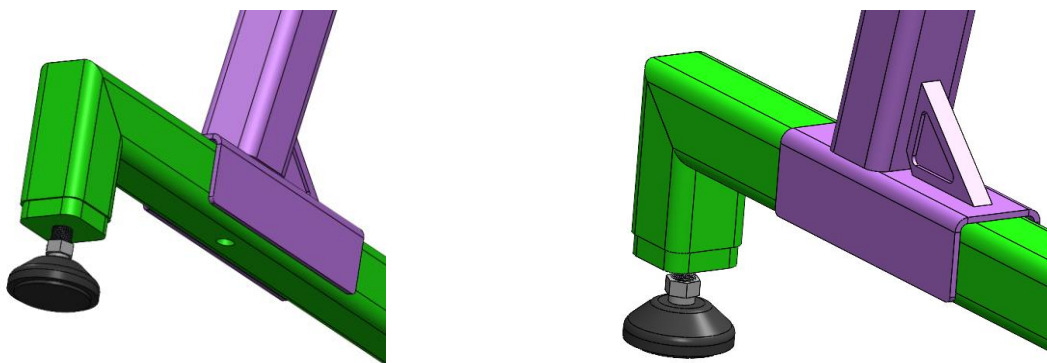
Vista inferior de la estructura base (Fuente 21)
